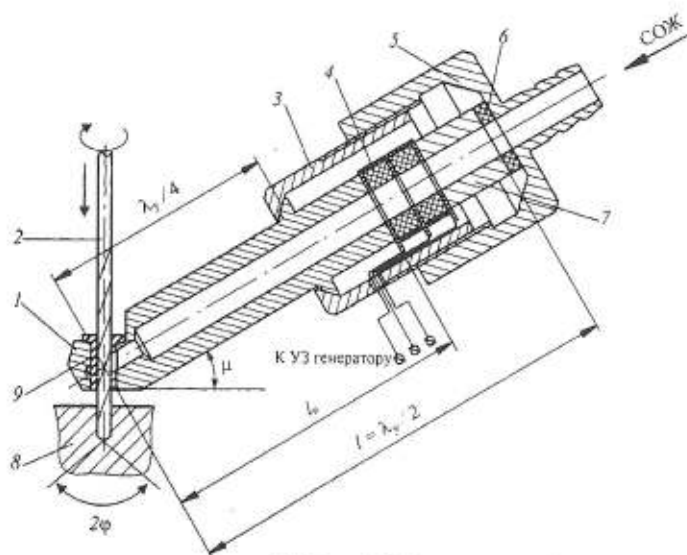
Устройство для наложения УЗК на СОЖ и сверло: 1 - волновод; 2 - сверло; 3 - стакан; 4 - пьезопреобразователь; 5 - штуцер; 6 - прокладка; 7 - отражающая шайба; 8 - заготовка
